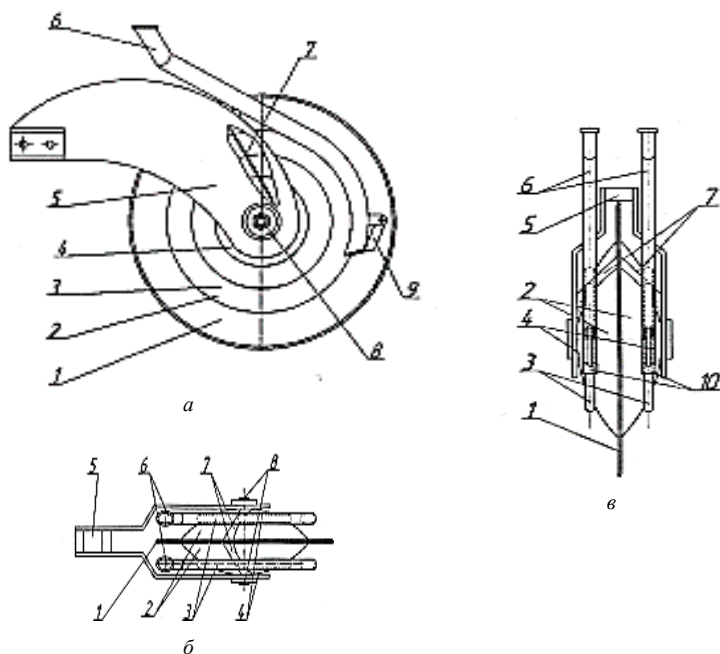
Комбинированный однодисковый сошник для узкорядного посева:
